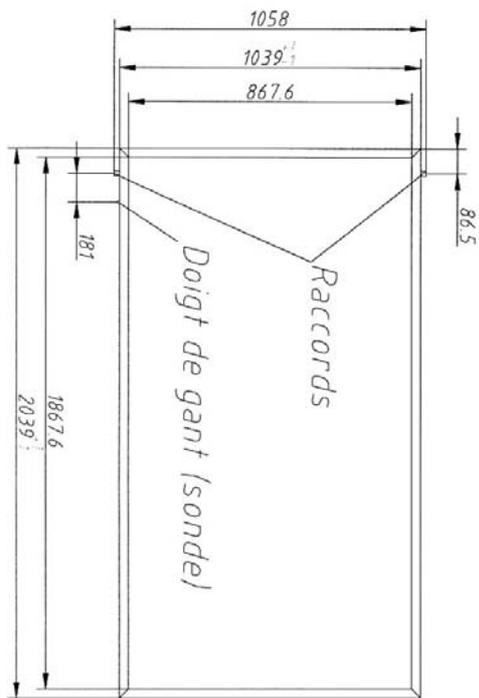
Capteur solaire "FK 7200 - vue en plan et en coupe
